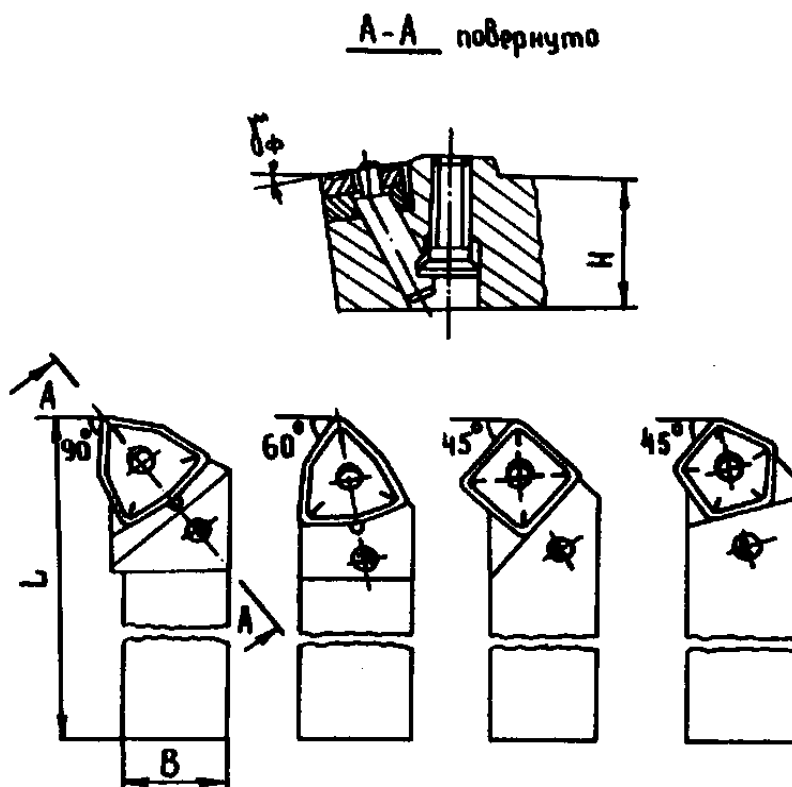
Резцы конструкции АМО - ЗИЛ
